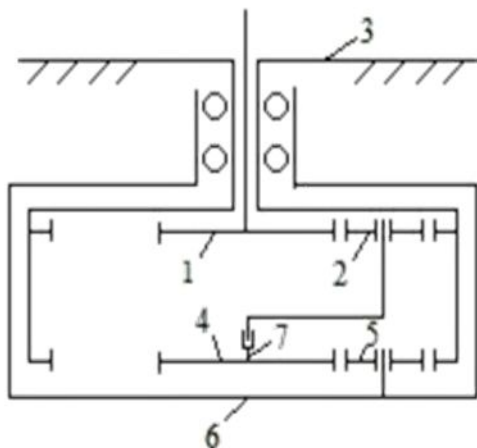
Кинематическая схема двухступенчатого планетарного редуктора: 1 – вал-шестерня 1^{ой} ступени; 2 – сателлит 1^{ой} ступени; 3 – эпициклическое колесо; 4 – шестерня 2^{ой} ступени; 5 – сателлит 2^{ой} ступени; 6 – водило 2^{ой} ступени; 7 – водило 1^{ой} ступени
